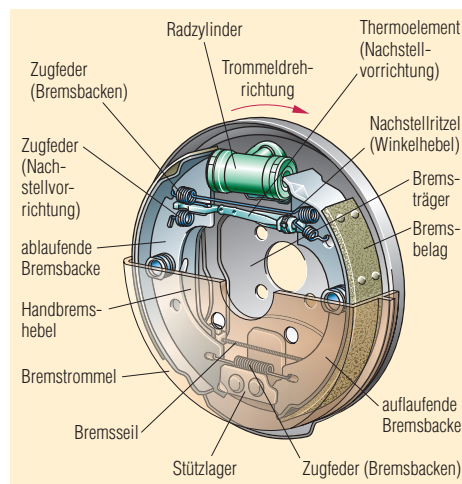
Prinzipieller Aufbau einer Pkw-Trommelbremse (rechtes Hinterrad).
